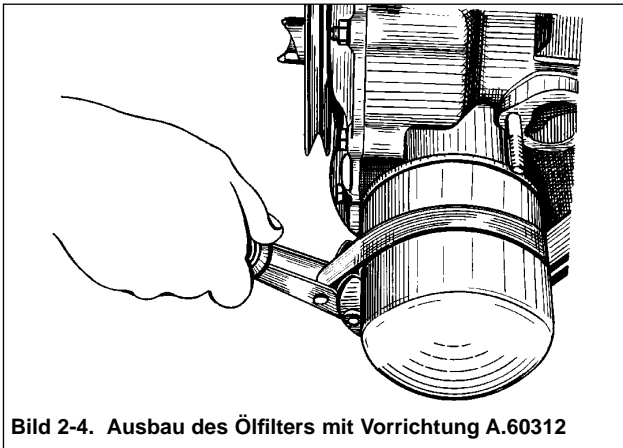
Ausbau des Ölfilters mit Vorrichtung A.60312
